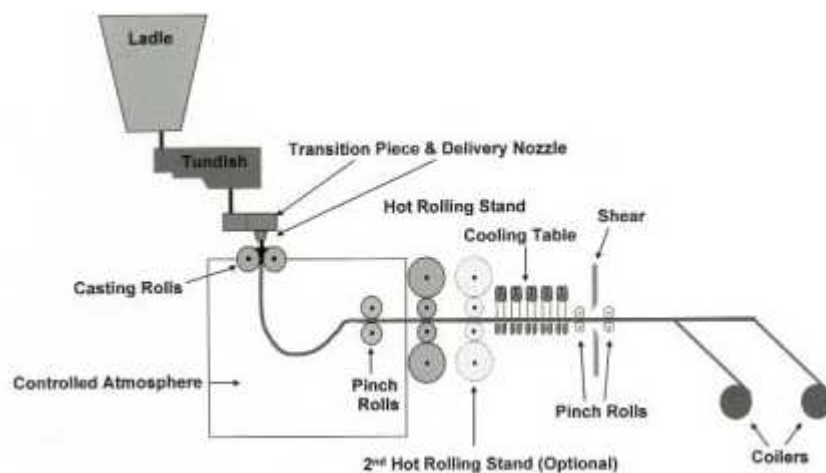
Especificaciones técnicas y vista esquemática de la planta de Castrip.
